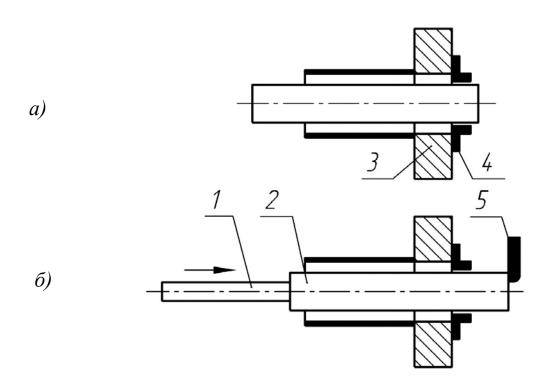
(начало). Цикл автоматической работы токарного станка с барфидером: I — толкатель; 2 — пруток; 3 — патрон станка; 4 — кулачки; 5 — упор; a — установка прутка в начале обработки; δ — проталкивание прутка до упора
